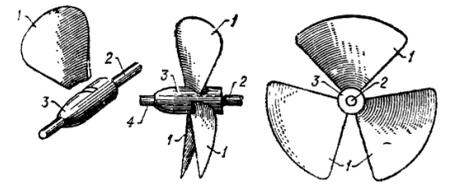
Детали винта насоса: 1 — лопасть; 2 — вал; 3 — ступица; 4 — свободный конец вала (вставляется в подшипник на крестовине)
